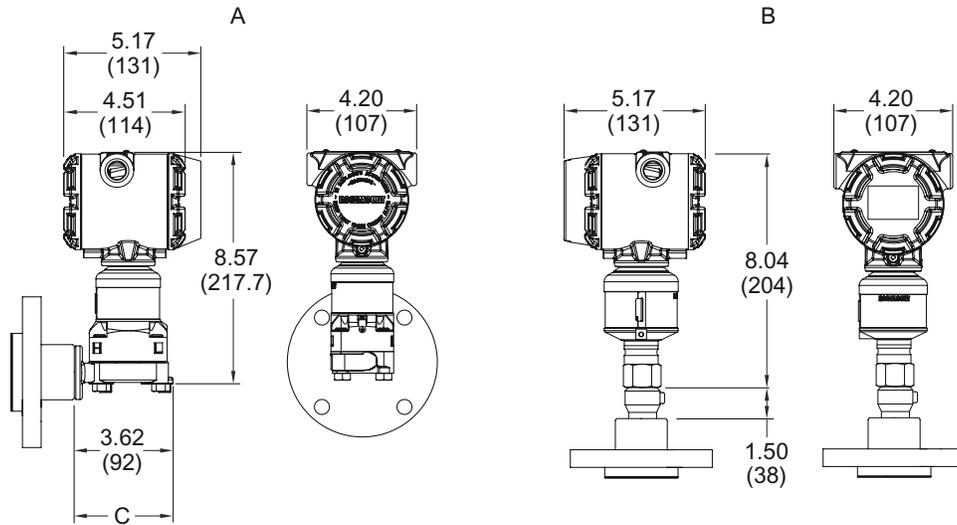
Skalierbarer Rosemount 3051S Messumformer für Füllstandsmessungen mit FF-Druckmittler
